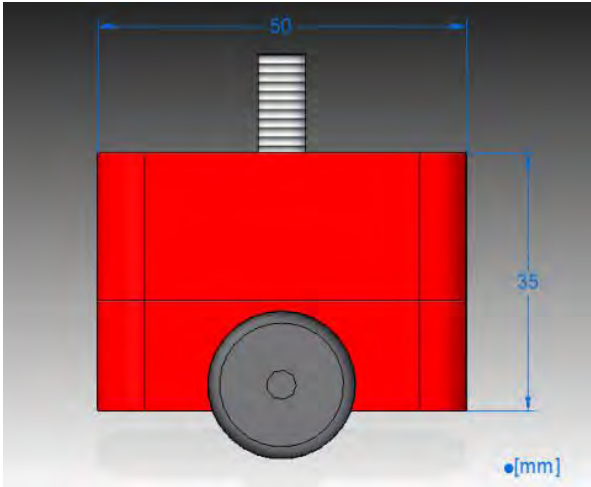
Dimensiones de las mordazas de tipo tornillo, vista frontal.
